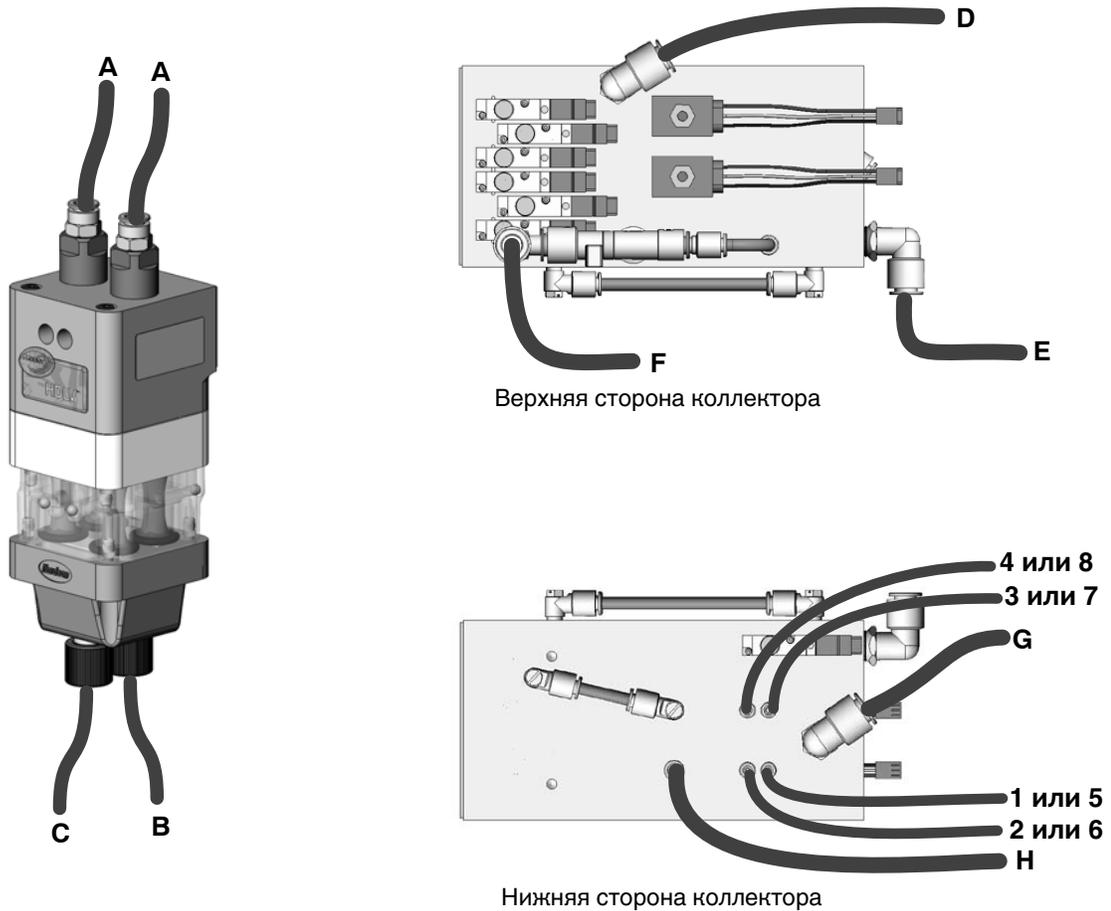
Номера деталей пневмошлангов и порошковых шлангов
